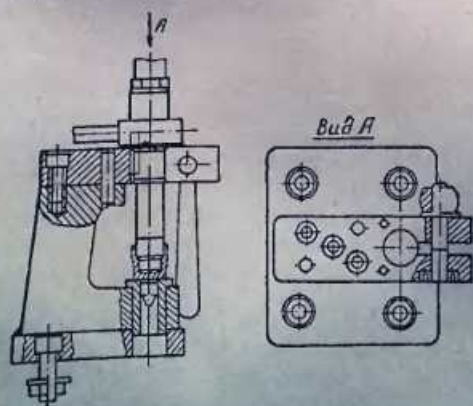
Приспособление ЛМ9690-171 для центровки распылителя
